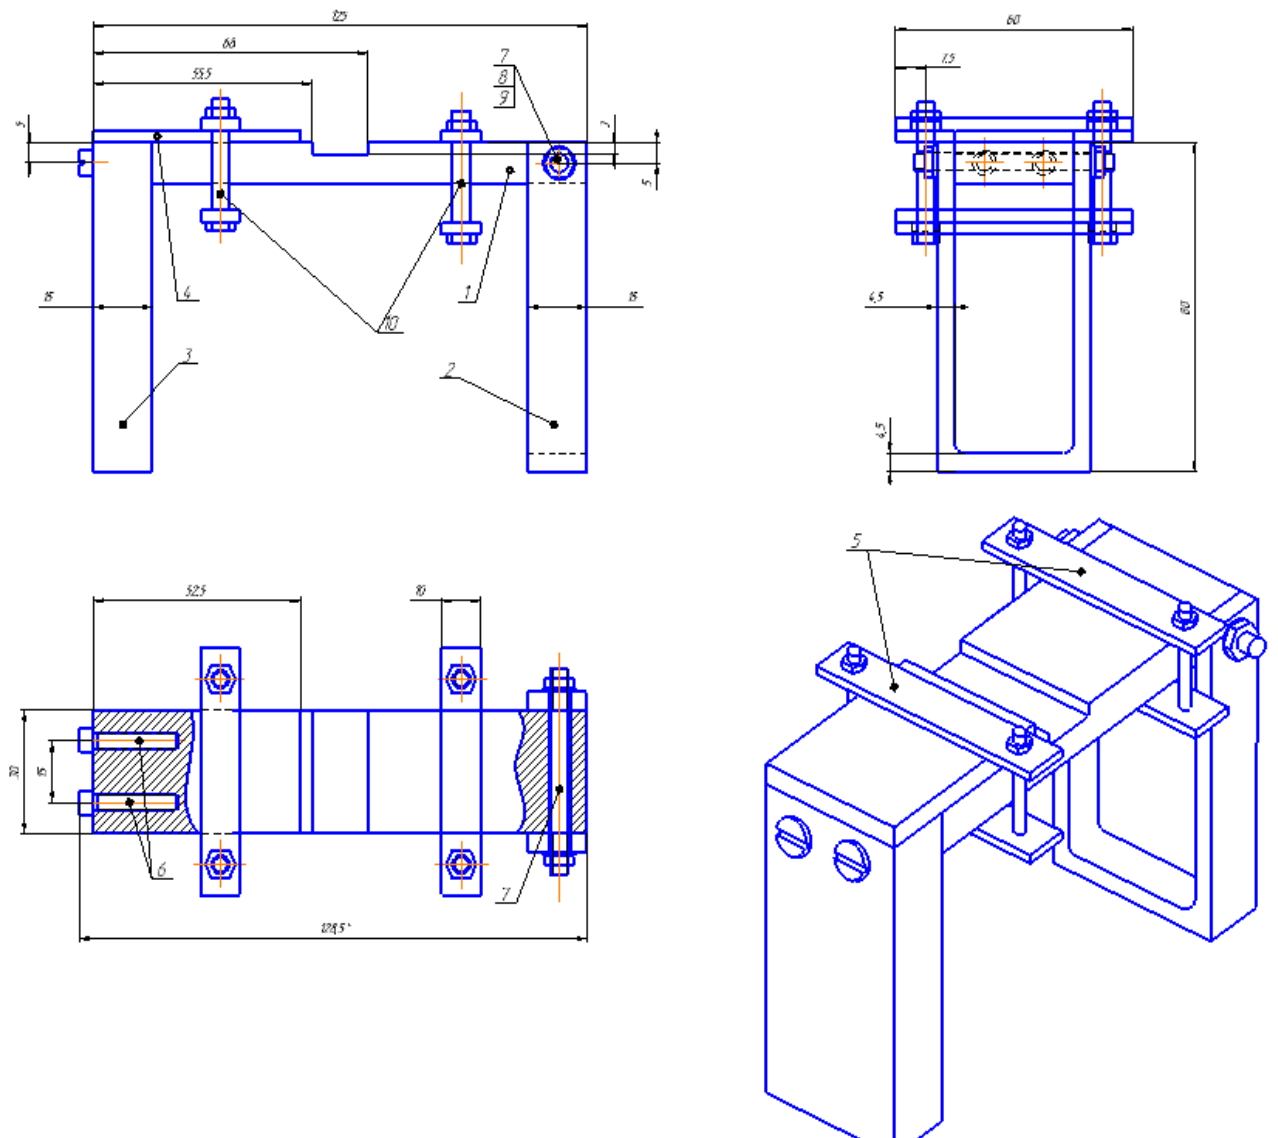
Приспособление для пайки изделий с нахлесточным соединением
